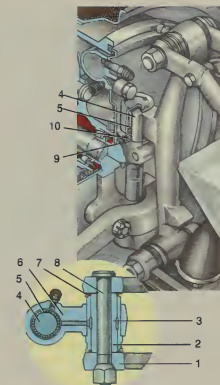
Узел передней подвески: 1 — нижний рычаг; 2 — распорная втулка; 3 — резьбовая втулка; 4 — шкворень; 5 — игольчатый подшипник шкворня; 6 — стойка; 7 — уплотнительное кольцо; 8 — палец; 9 — уплотнитель упорного подшипника; 10 — упорный подшипник.
